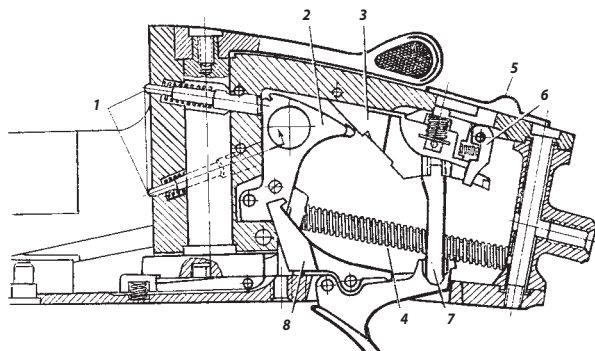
Механизм ружья Иж-12: 1 — бойки; 2 — курок; 3 — шептало; 4 — боевая пружина на стержне; 5 — кнопка предохранителя; 6 — флажки предохранителя; 7 — промежуточная тяга; 8 — интерсептор
